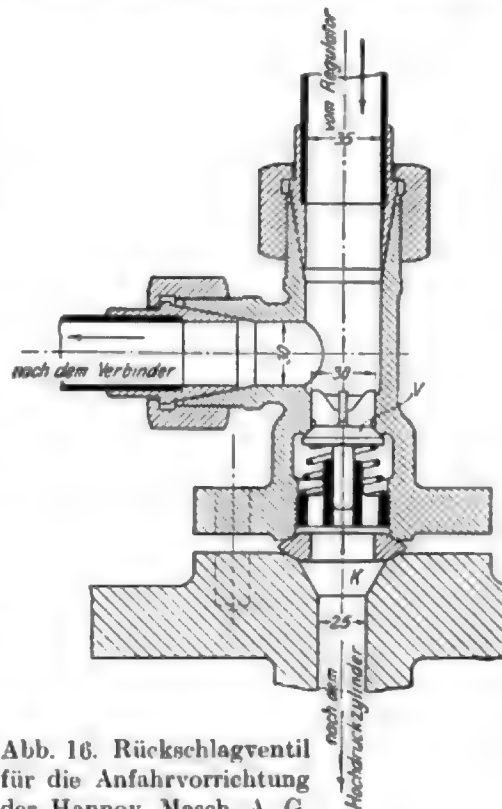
Rückschlagventil für die Anfahrvorrichtung der Hannov. Masch.-A.-G.
